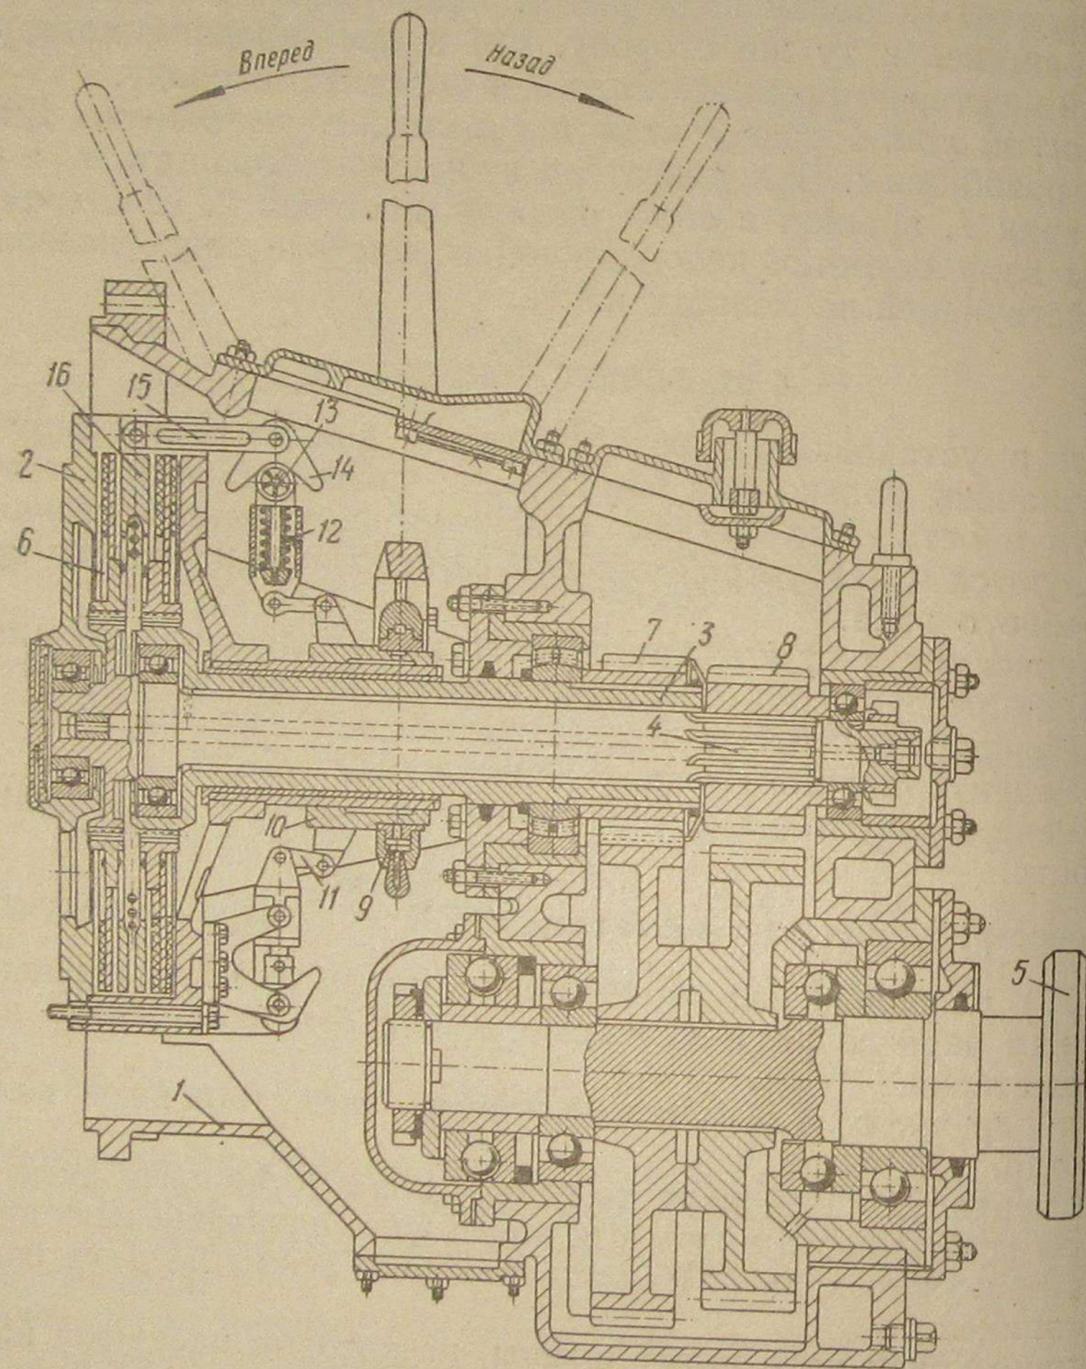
Реверс-редуктор двигателя 6ГСЧ $\frac{15,0}{18,0}$ (ЗД-6-ГД)
